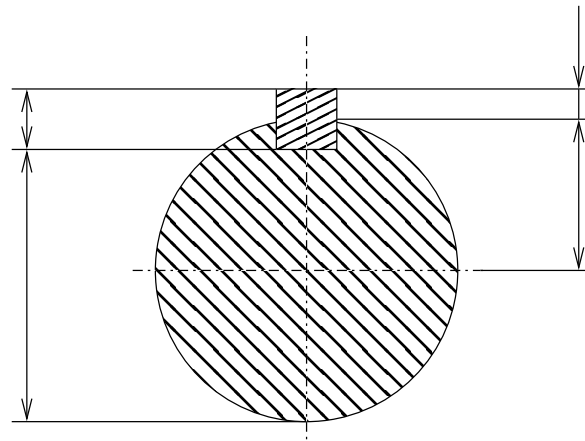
Vue en coupe d'un des 2 arbres et de sa clavette à compléter.
